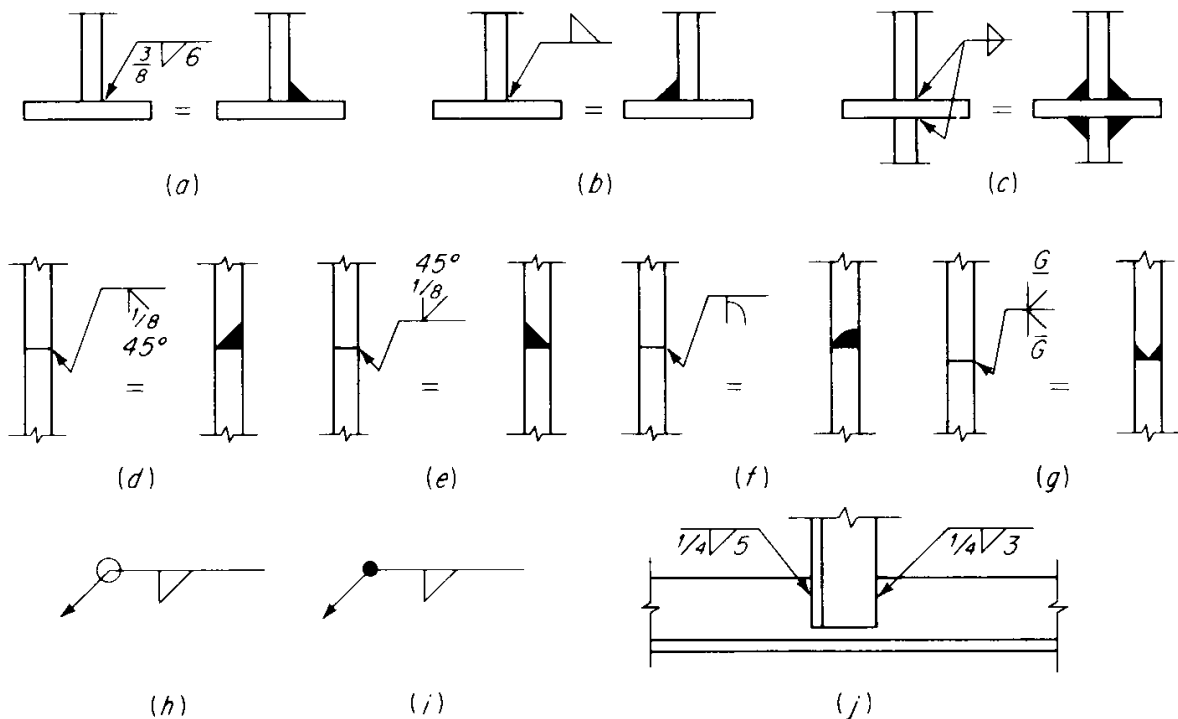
Ejemplos de símbolos de soldadura (Ref. 2)
